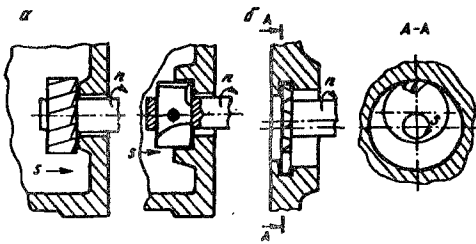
Компоненты корпусных деталей, нетехнологичные для обработки на станках с ЧПУ
